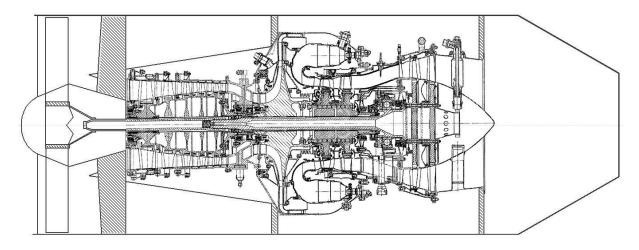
Вариант схемы ТРДД на базе газогенератора двигателя ТВ7-117
